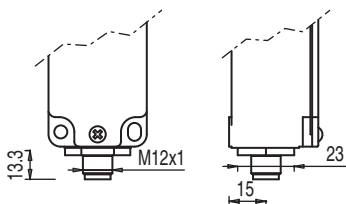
Dimensioni dell'S300-P13C1-M12-xxx in mm (qui dimensioni del connettore M12)
